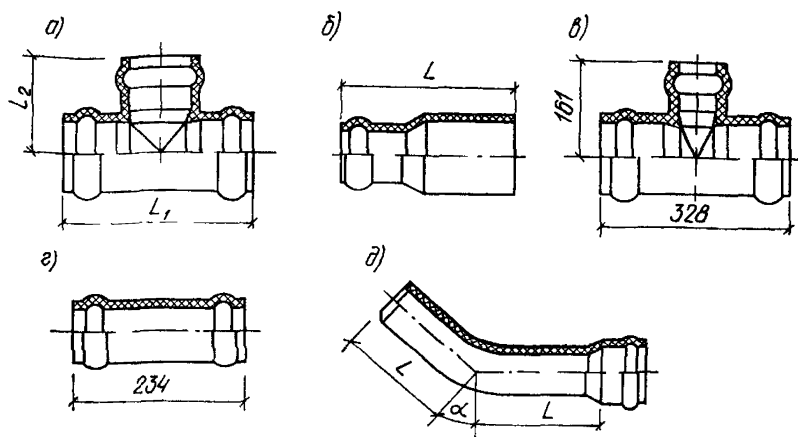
Соединительные детали из ПВХ для раструбных труб:
